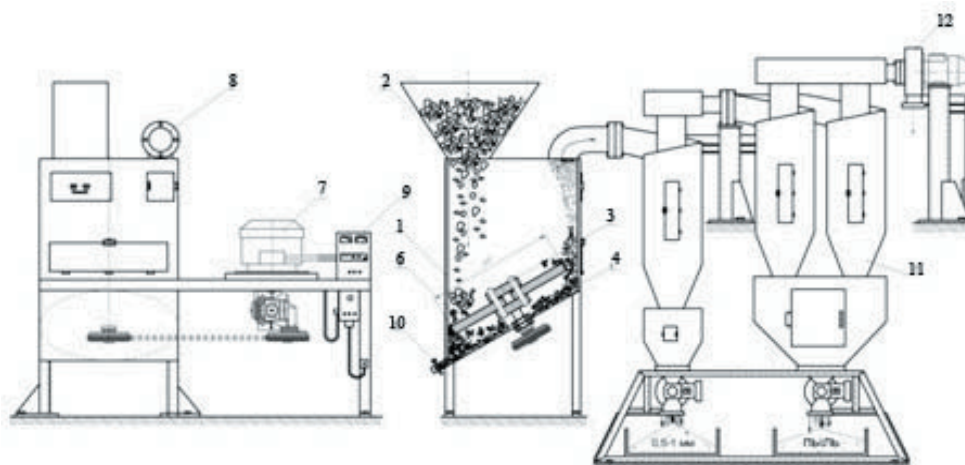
Конструкція установки диспергатора-подрібнювача: 1 – рамний корпус; 2 – завантажувальний желоб; 3 – патрубок для вивантаження; 4 – ротор; 5 – диск кріплення біл; 6 – біло (робочий орган диспергатора); 7 – електропривод; 8 – клино-ремена передача; 9 – шкаф керування; 10 – механізм вилучення тіл, що не подрібнені; 11 – повітряний класифікатор; 12 – транспортний вентилятор
